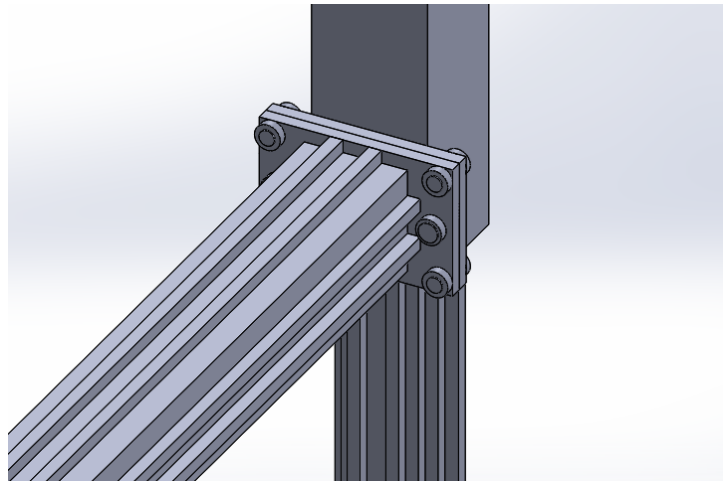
Detalhe da Fixação entre Viga de Elevação e Translação
